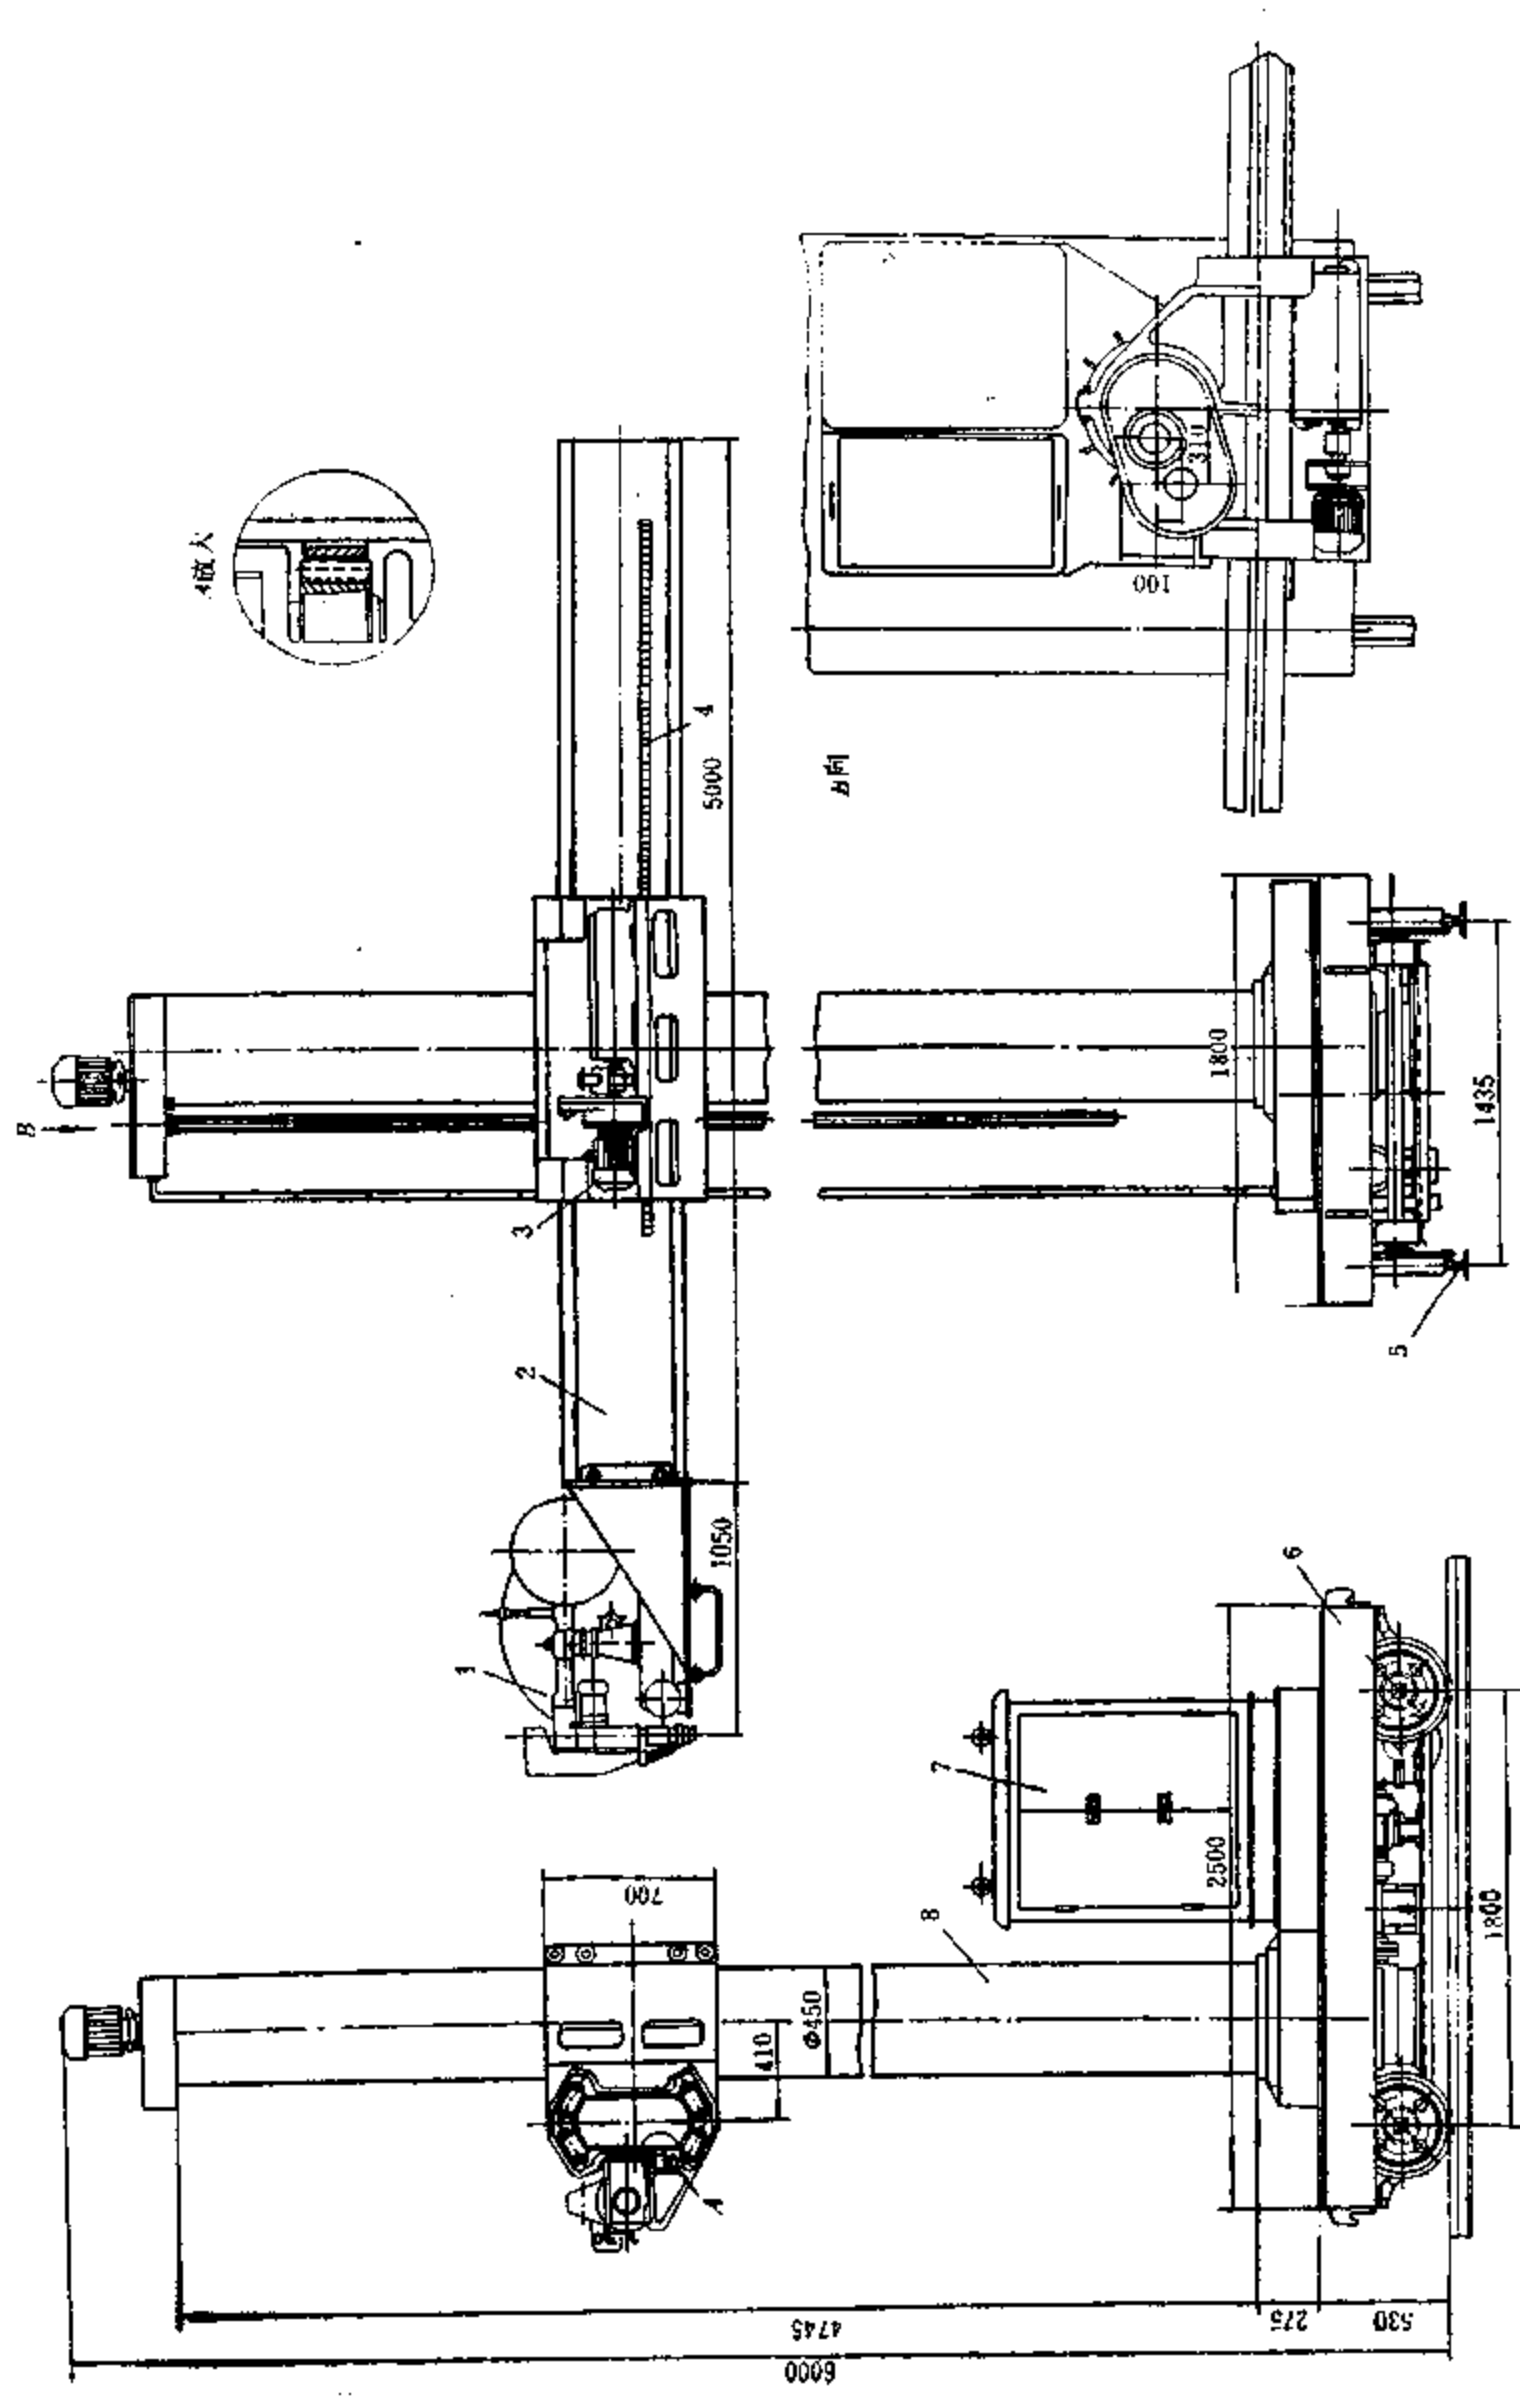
可伸缩的摇(悬)臂式焊接操作机
